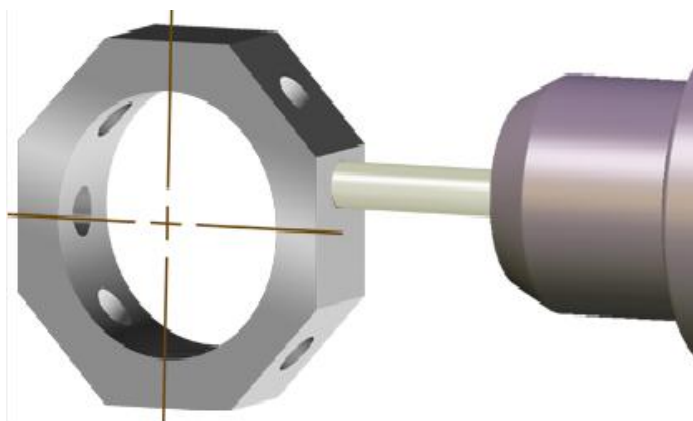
Vrtání děr v radiálním směru v ose rotace obrobku
